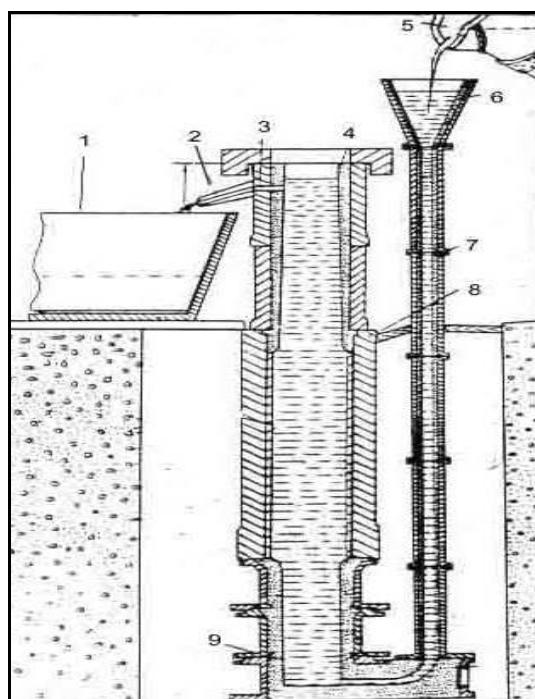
Схема литейной формы двухслойного валка: 1 – приемная мульда; 2 – желоб; 3 – сливная летка; 4 – форма верхней шейки; 5 – ковш; 6 – воронка; 7 – стояк; 8 – кокиль; 9 – форма нижней шейки
